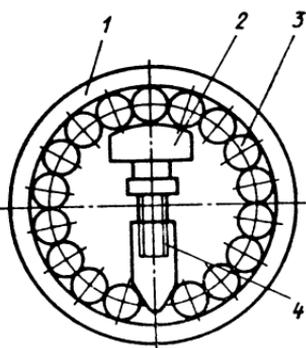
Приспособление для плавного опускания и установки детали на станке
